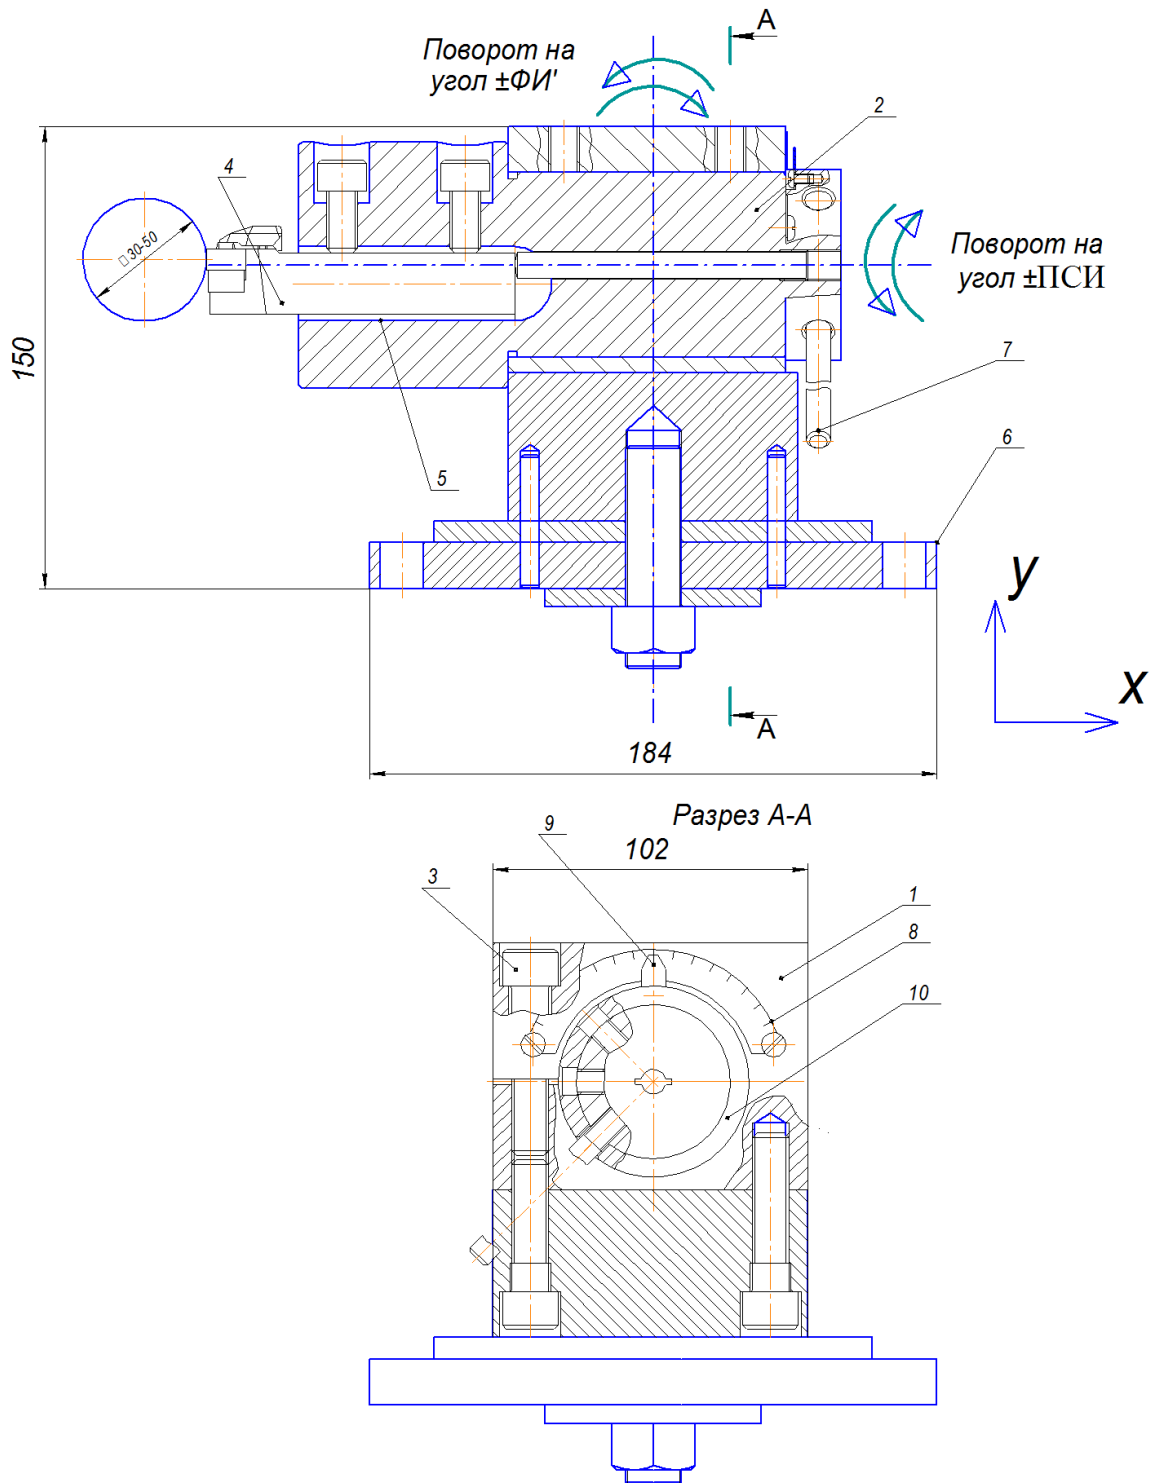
Сборочный чертеж технологического приспособления для обработки выглаживанием с применением СМП.
